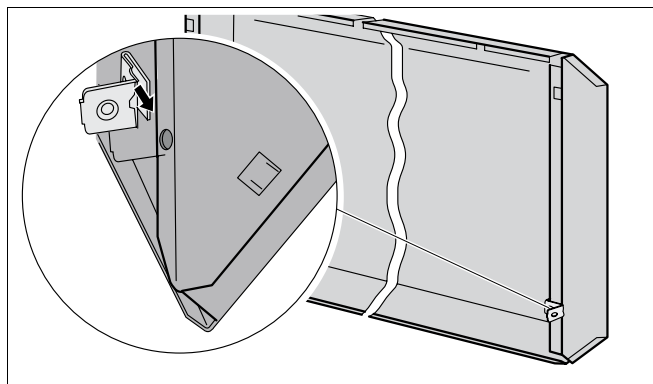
Установка гайки с защелкой (здесь: на правой боковой стенке)
